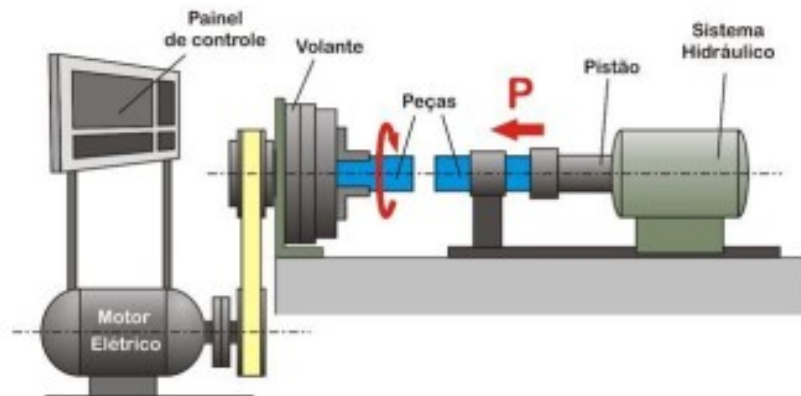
Equipamento de soldagem por Fricção Inercial
